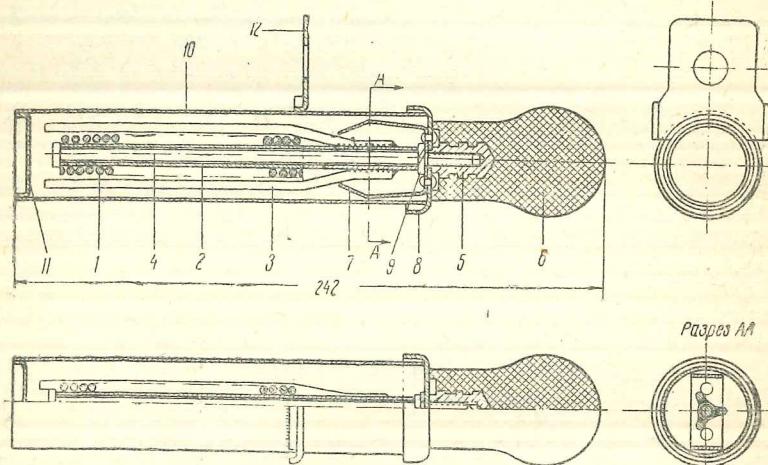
Вентилятор для розжига топлива газогенераторной установки ГАЗ-42.
